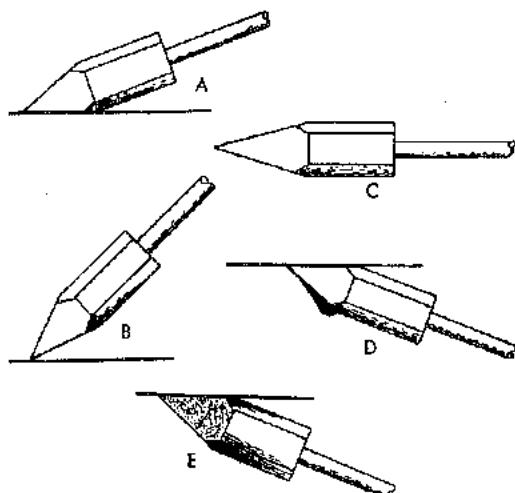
Formas y métodos de aplicación del soldador.
